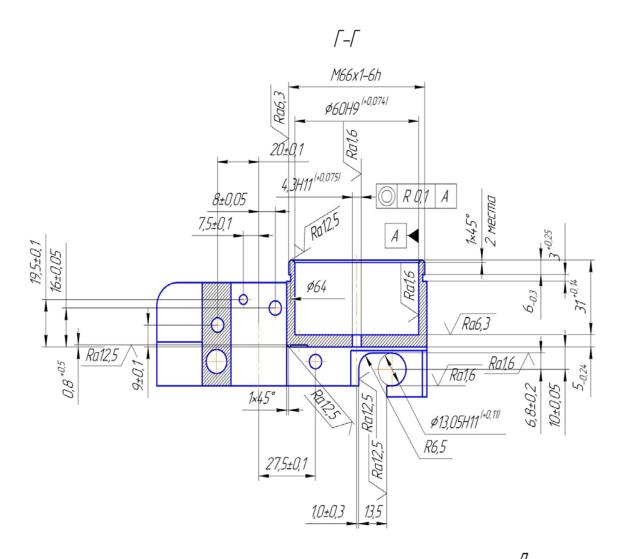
Чертеж детали «Корпус» (см. также с. 157 и 158)
